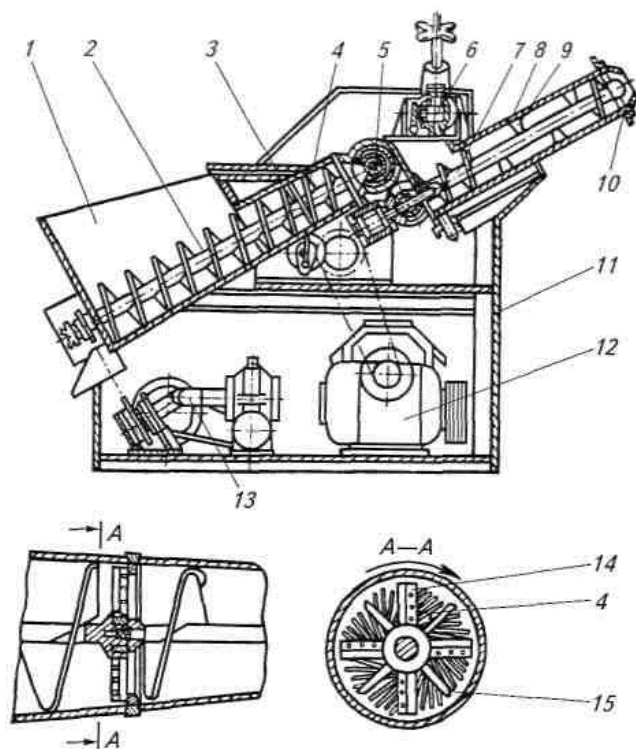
Дозатор-смеситель: 1 — бункер; 2 — подающий шнек; 3 — измельчитель; 4—решетка; 5 — дозатор творога; 6 — дозатор сливок; 7—шнек смесителя; 8 — смеситель; 9 — вал смесителя с лопатками; 10— насадка; 11 — станина; 12 — привод дозатора; 13 — привод подающего шнека; 14 — лопатка; 15 — нож
